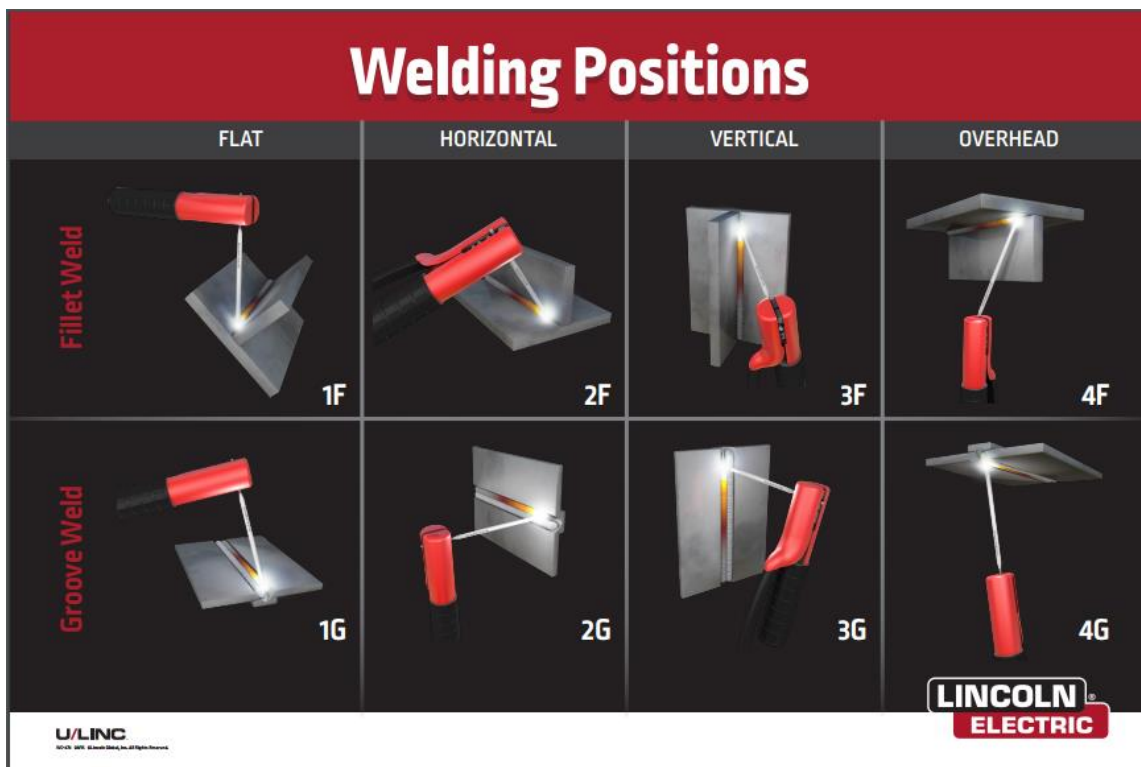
Posiciones para soldaduras de filete y bisel.
